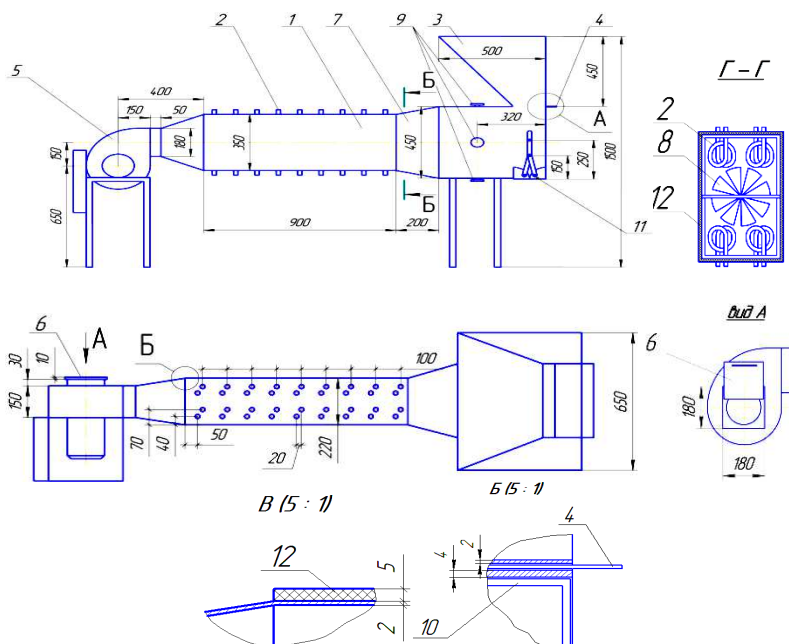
Чертеж устройства для тепловой обработки зерна:
